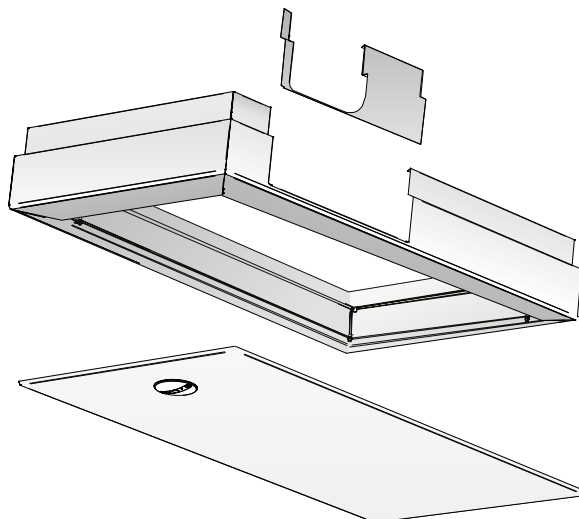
Designmodul mit zugehörigem Abdeckblech sowie Unterblech mit WISE SMB.
